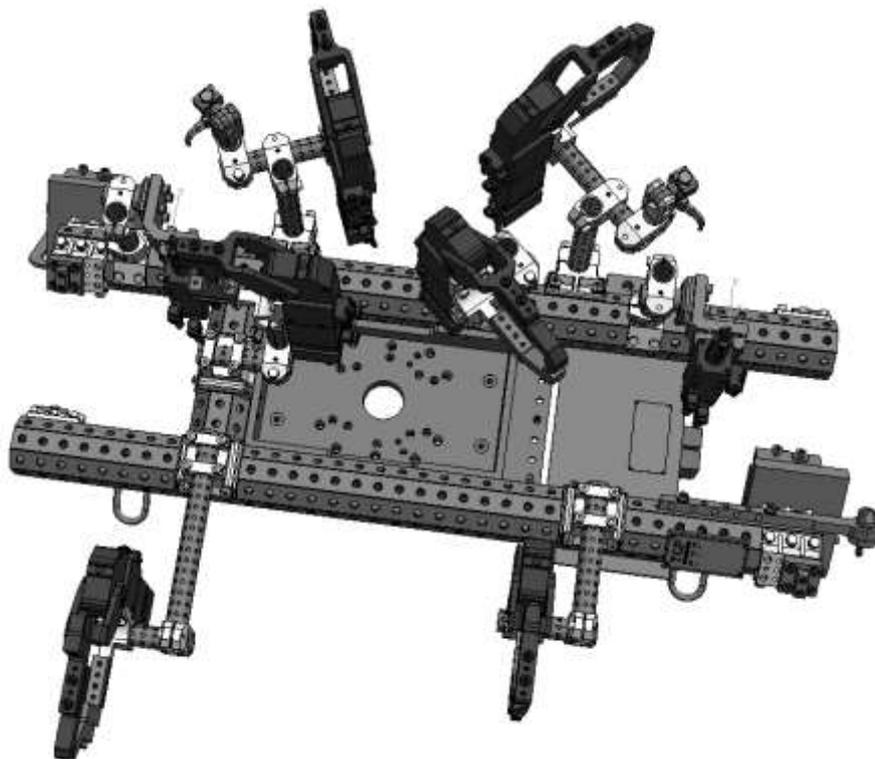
Внешний вид захвата в сборе (вид спереди)
